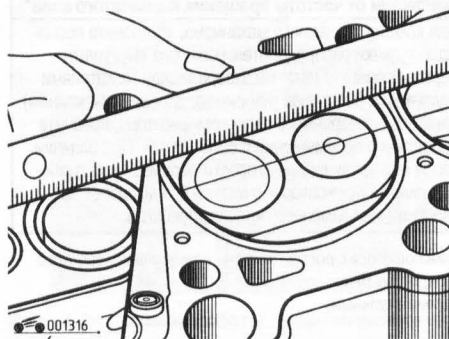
Проверка плоскостности привалочной поверхности головки блока цилиндров
